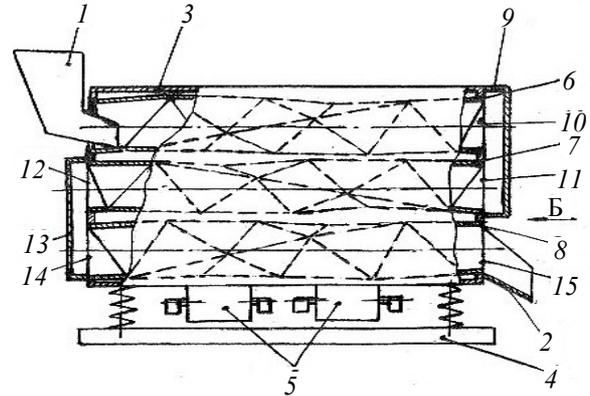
Станок с ярусно расположенными винтовыми роторами
